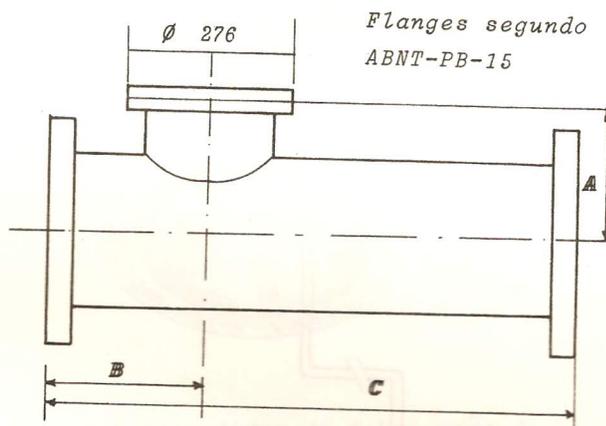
Dimensões do corpo do macromedidor - L.A.O.
